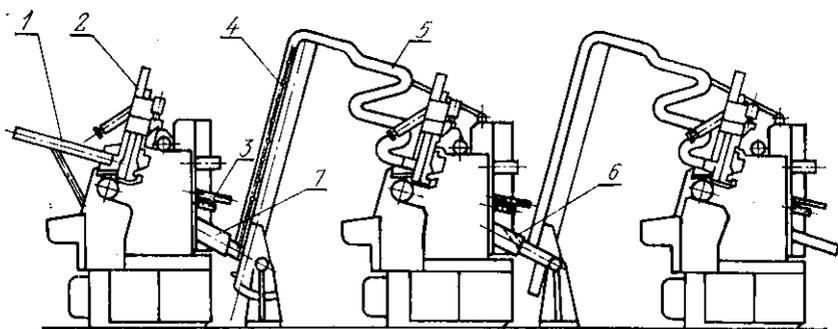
Схема автоматической линии для токарной обработки ведущей шестерни автомобиля
